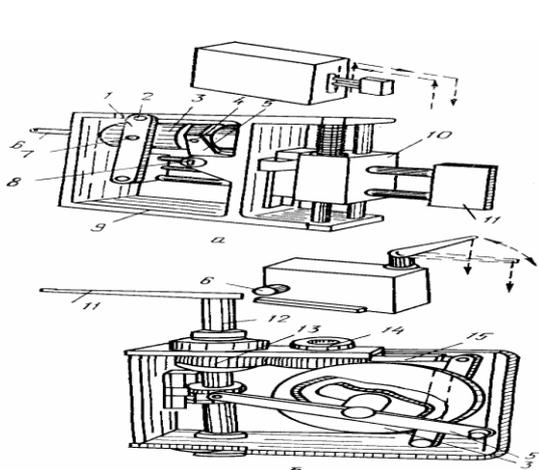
Сборочные головки фирмы Ferguson: а — с линейными движениями исполнительного устройства; б — с поворотом устанавливаемой детали
